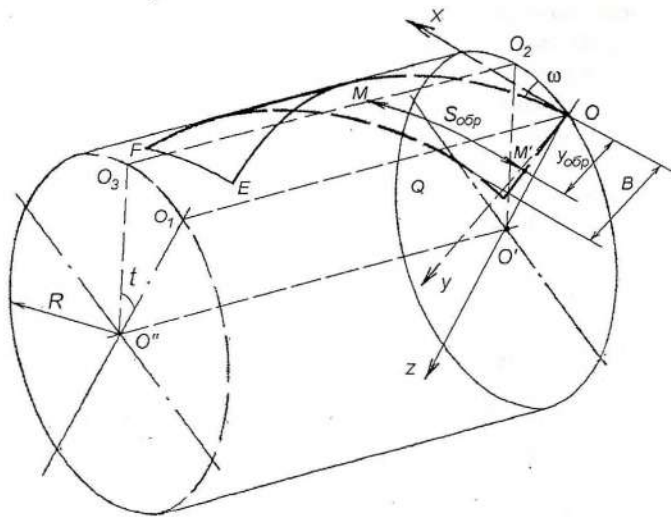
Образование рабочей поверхности пластины отвала на основе круговой цилиндрической поверхности:  $B$  – ширина пластины;  $R$  – радиус несущего цилиндра;  $\omega$  – угол подъема винтовых линий;  $y_{обр}$  – координата текущей образующей;  $S_{обр}$  – длина винтовой образующей  $M'O$ .
